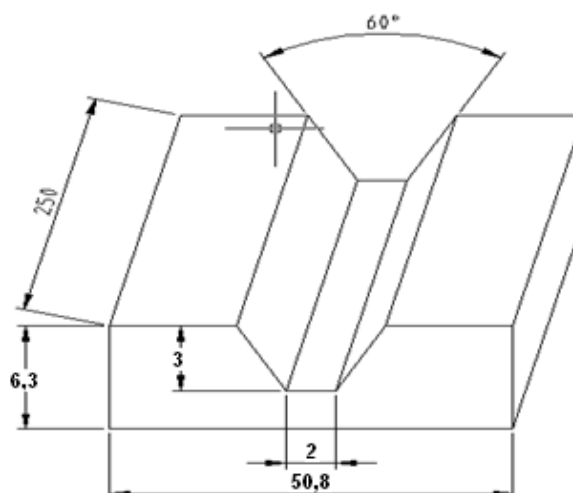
Desenho esquemático e dimensões (mm) da placa de teste
